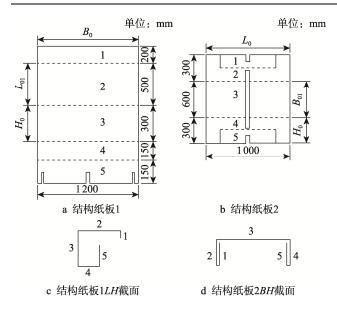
2 种结构纸板设计和截面示意图 Fig.1 Design and section sketches of boards with two structures
